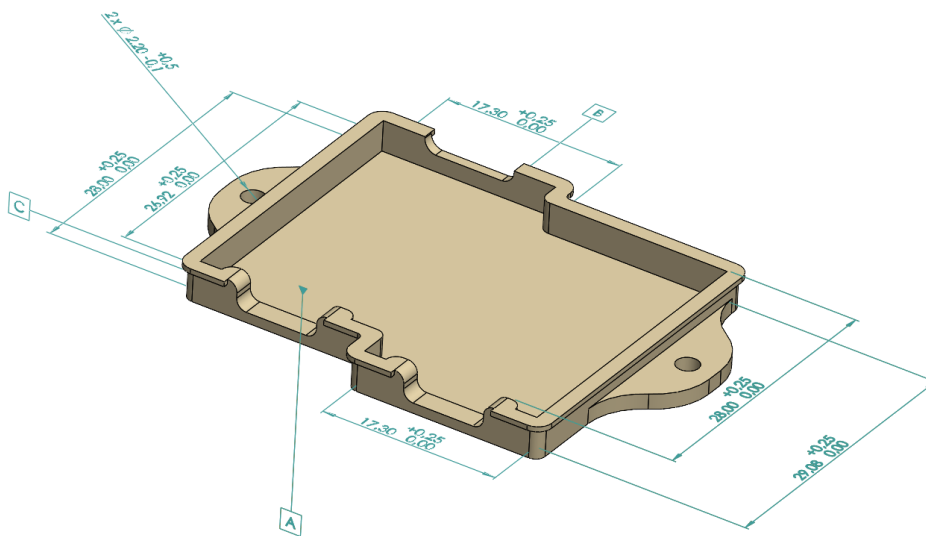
Tolerancias dimensionales “Carcasa TP4056”
